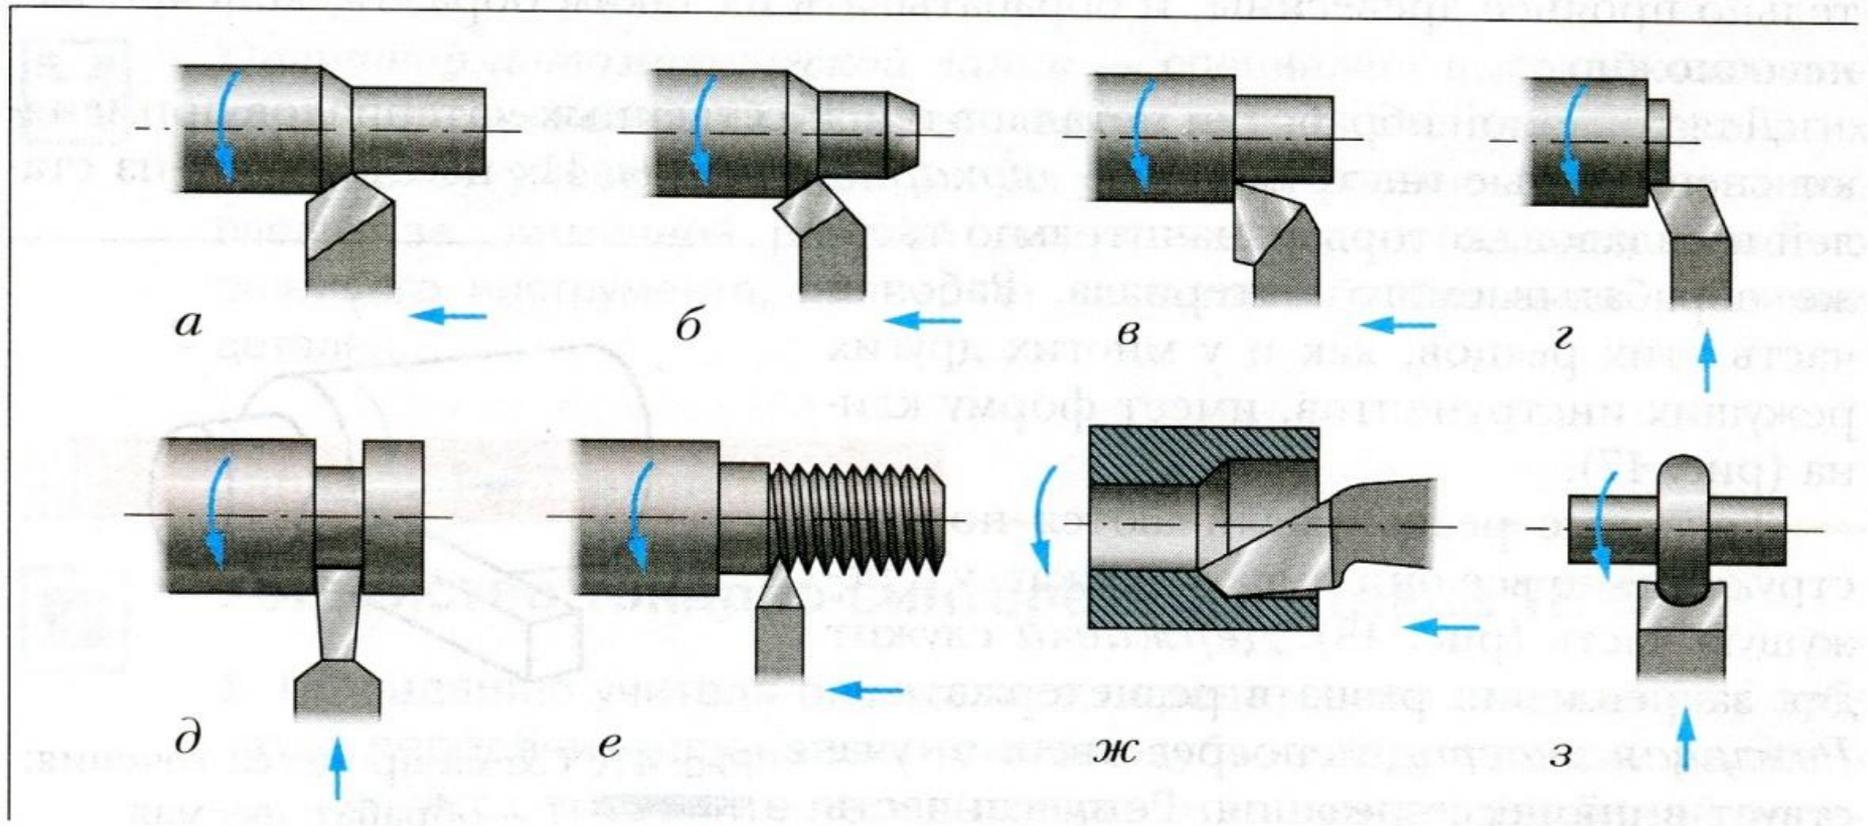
Токарные резцы: *a* — проходной прямой; *б* — проходной отогнутый; *в* — проходной упорный; *г* — подрезной; *д* — отрезной; *е* — резьбовой; *ж* — проходной расточной; *з* — фасонный
